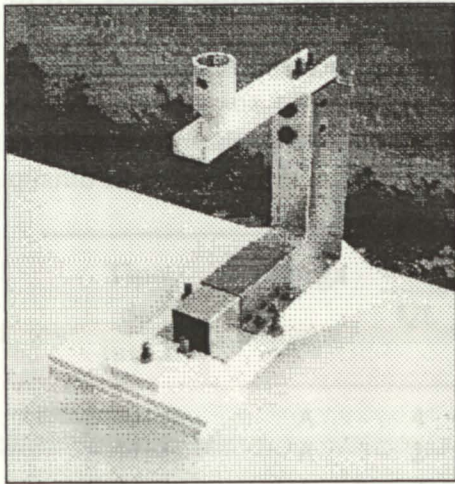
Cargas ensaiadas: A (junta soldada), B (junta reforçada)
